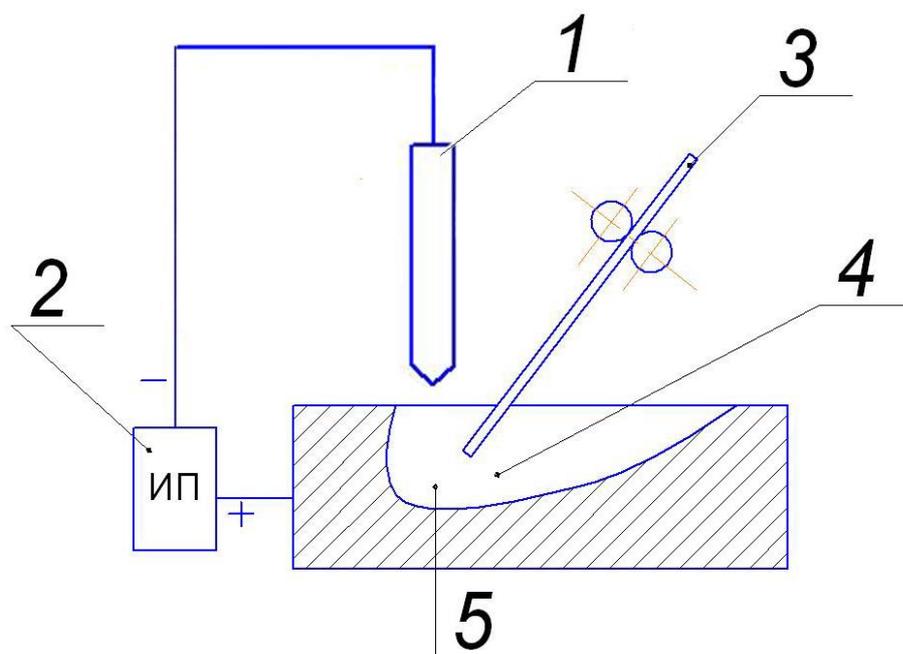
Схема способа механизированной сварки неплавящимся электродом в среде защитных газов с введением присадочной проволоки в хвостовую часть сварочной ванны. 1 – неплавящийся электрод, 2 – источник питания; 3 – присадочная проволока, 4 – хвостовая часть сварочной ванны, 5 – перегретый жидкий металл сварочной ванны
